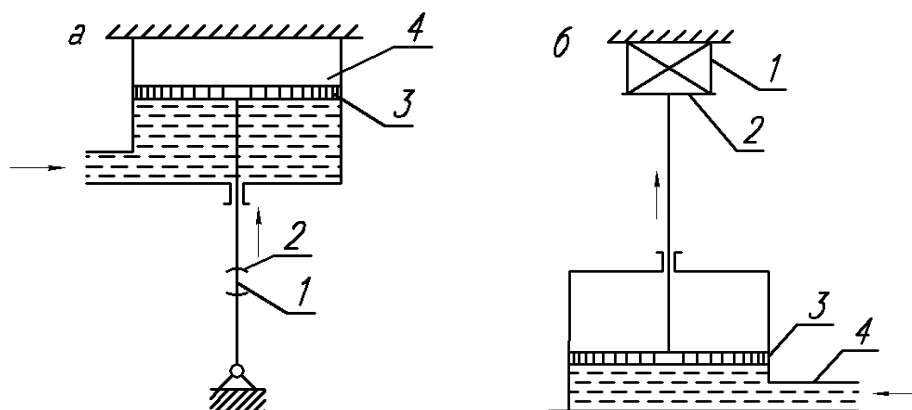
Схема машины с гидравлическим приводом: 1 – образец; 2 – подвижный захват; 3 – поршень; 4 – рабочий цилиндр
